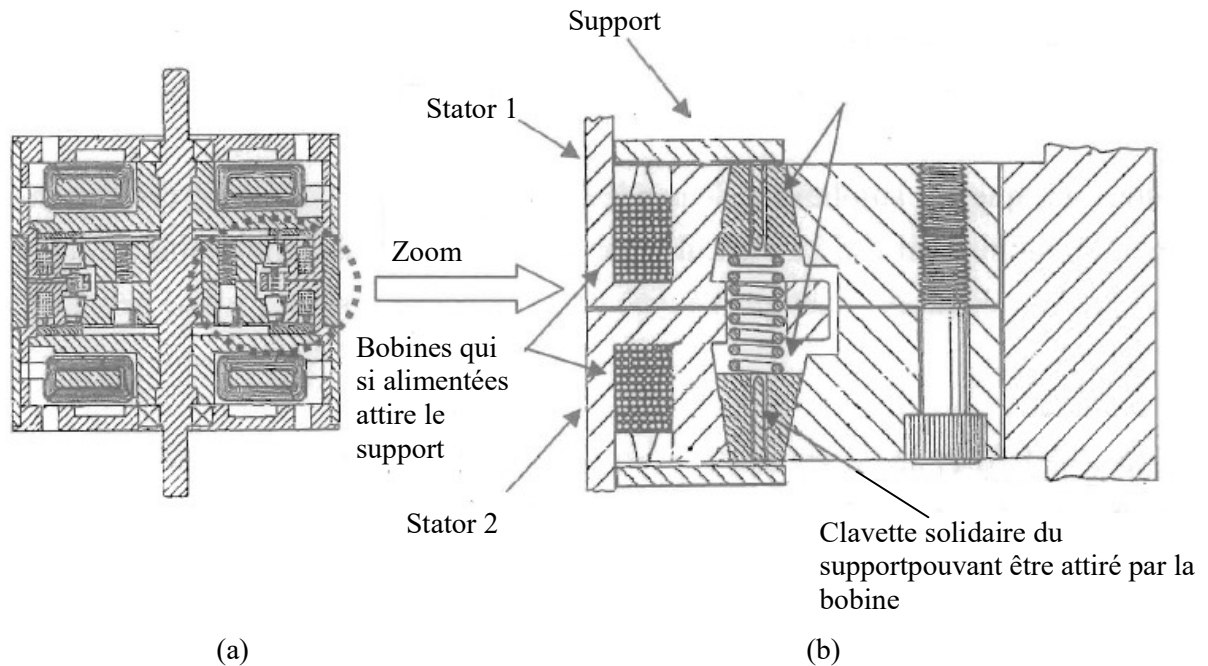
Moteur de Vranish : (a) vue latérale (b) vue de la partie active
